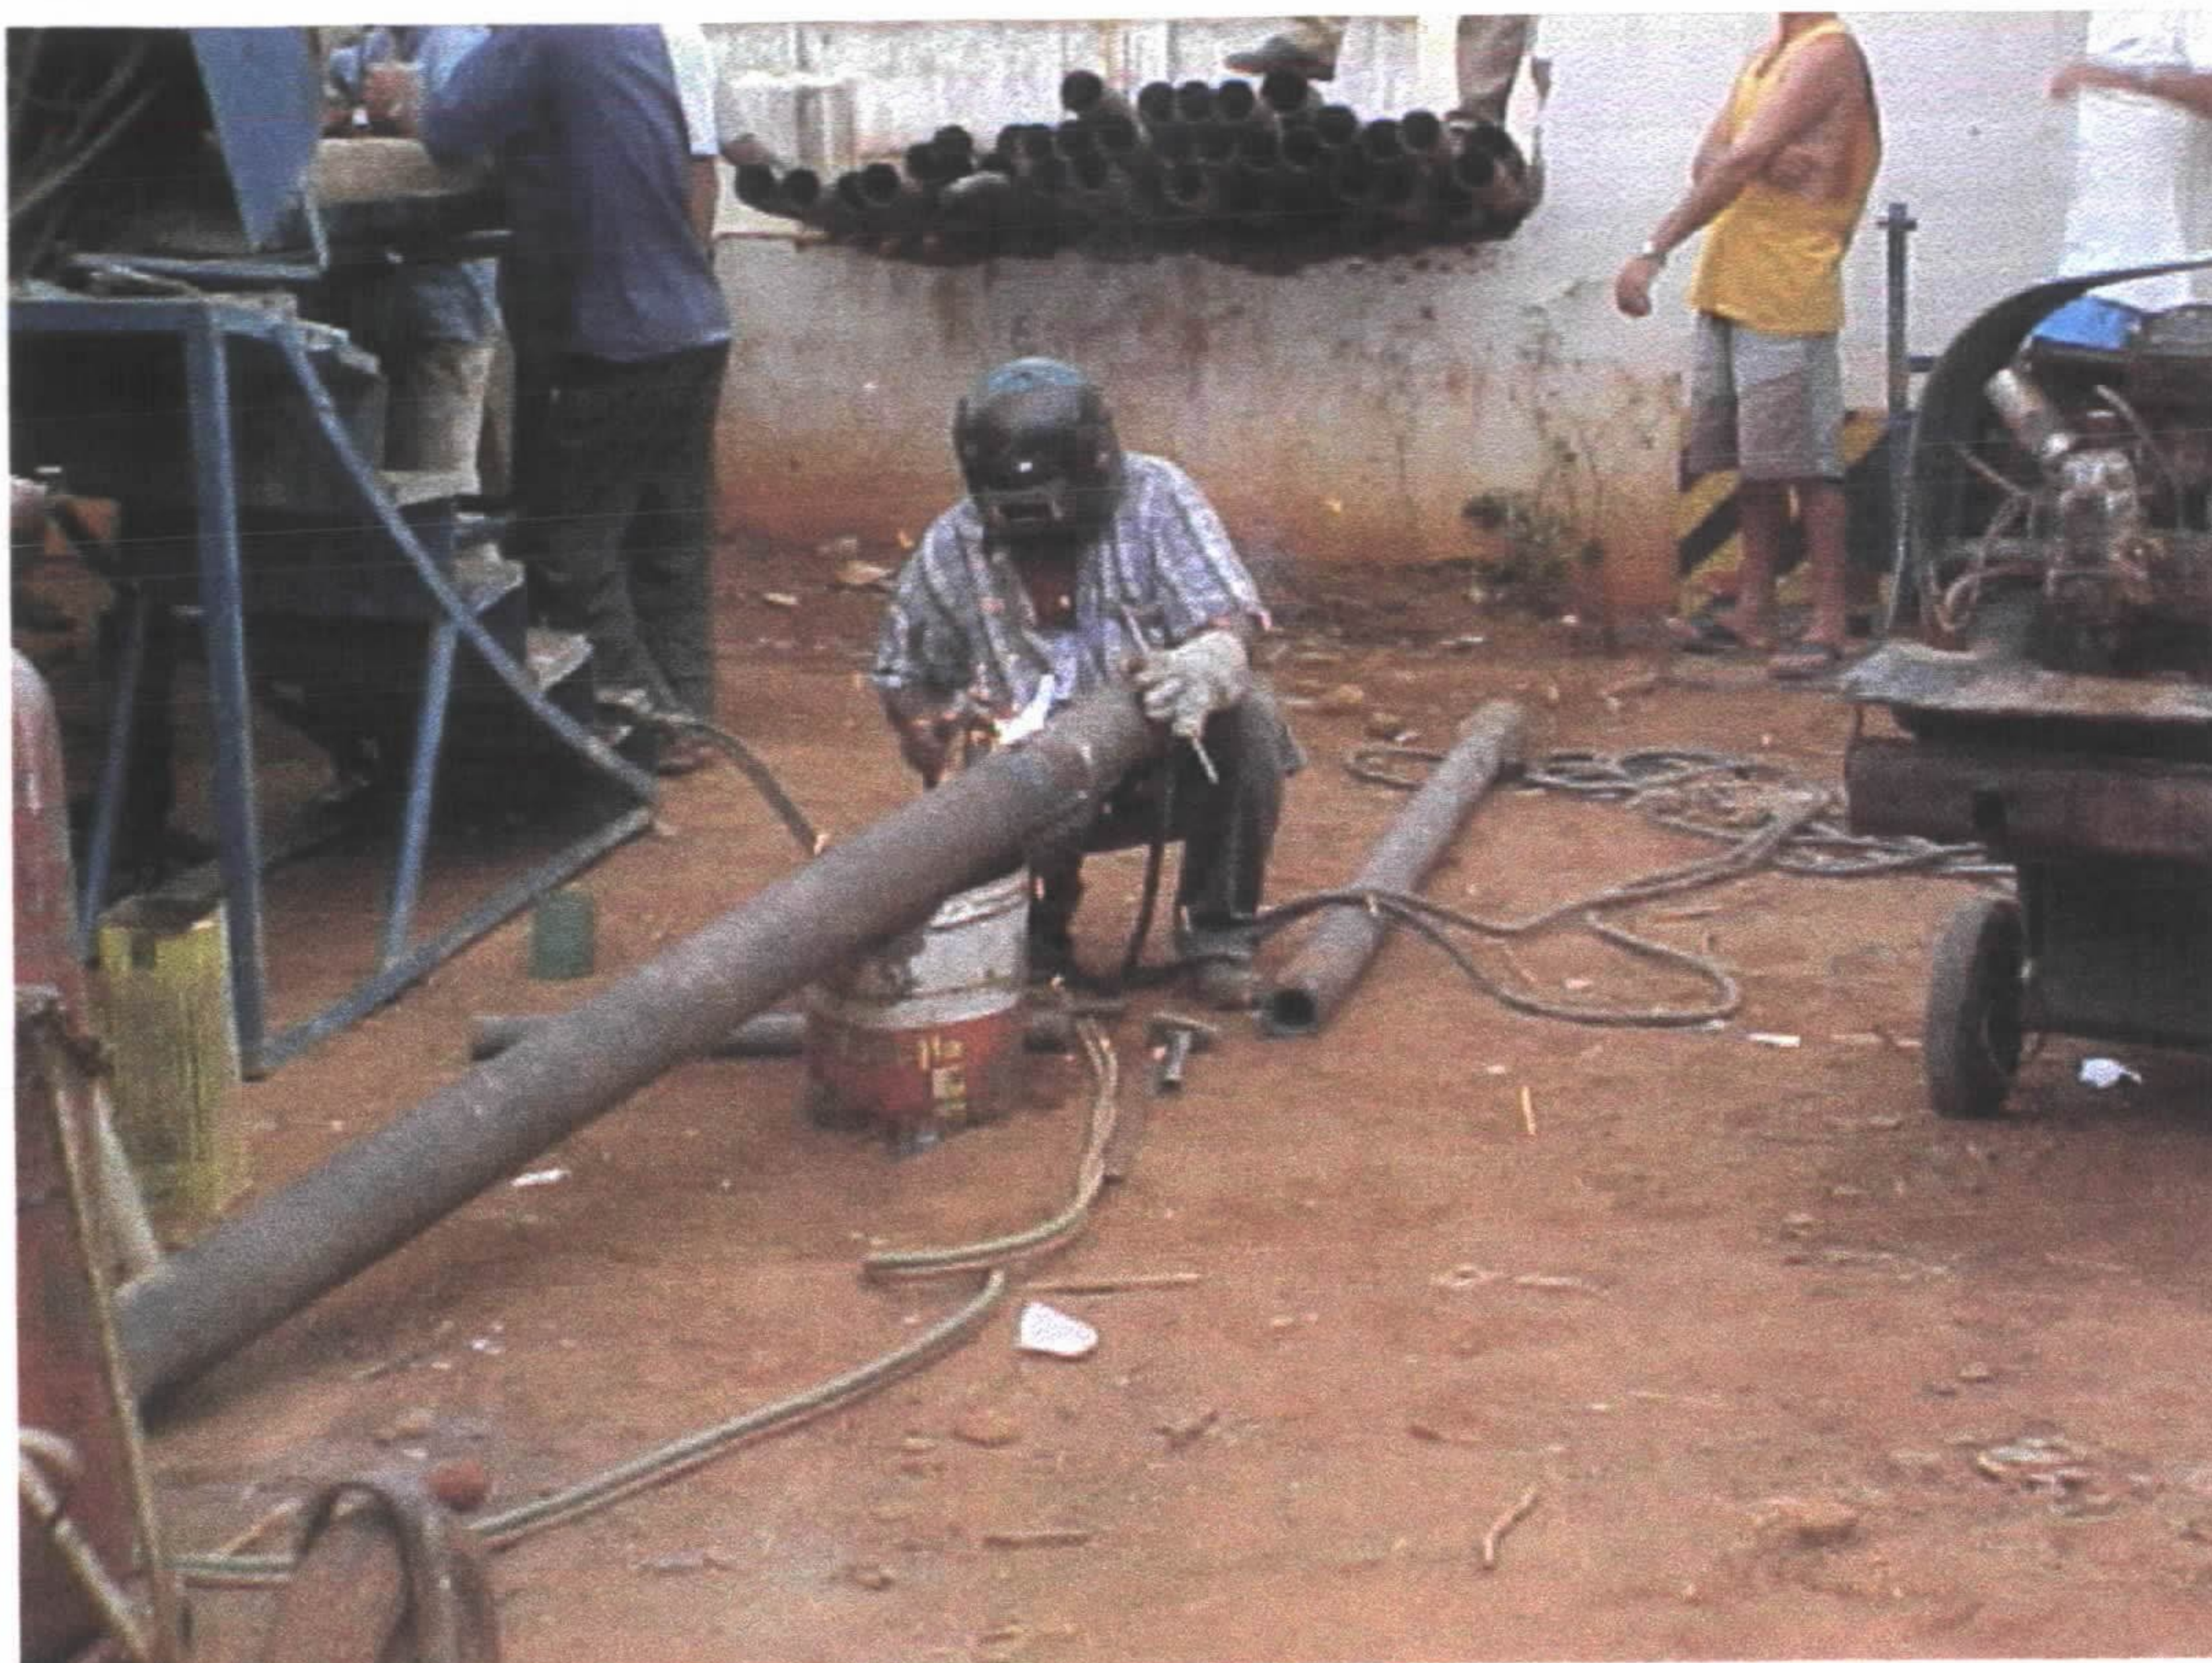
Detalhe da sapata utilizada nos trabalhos de corte/pescaria
